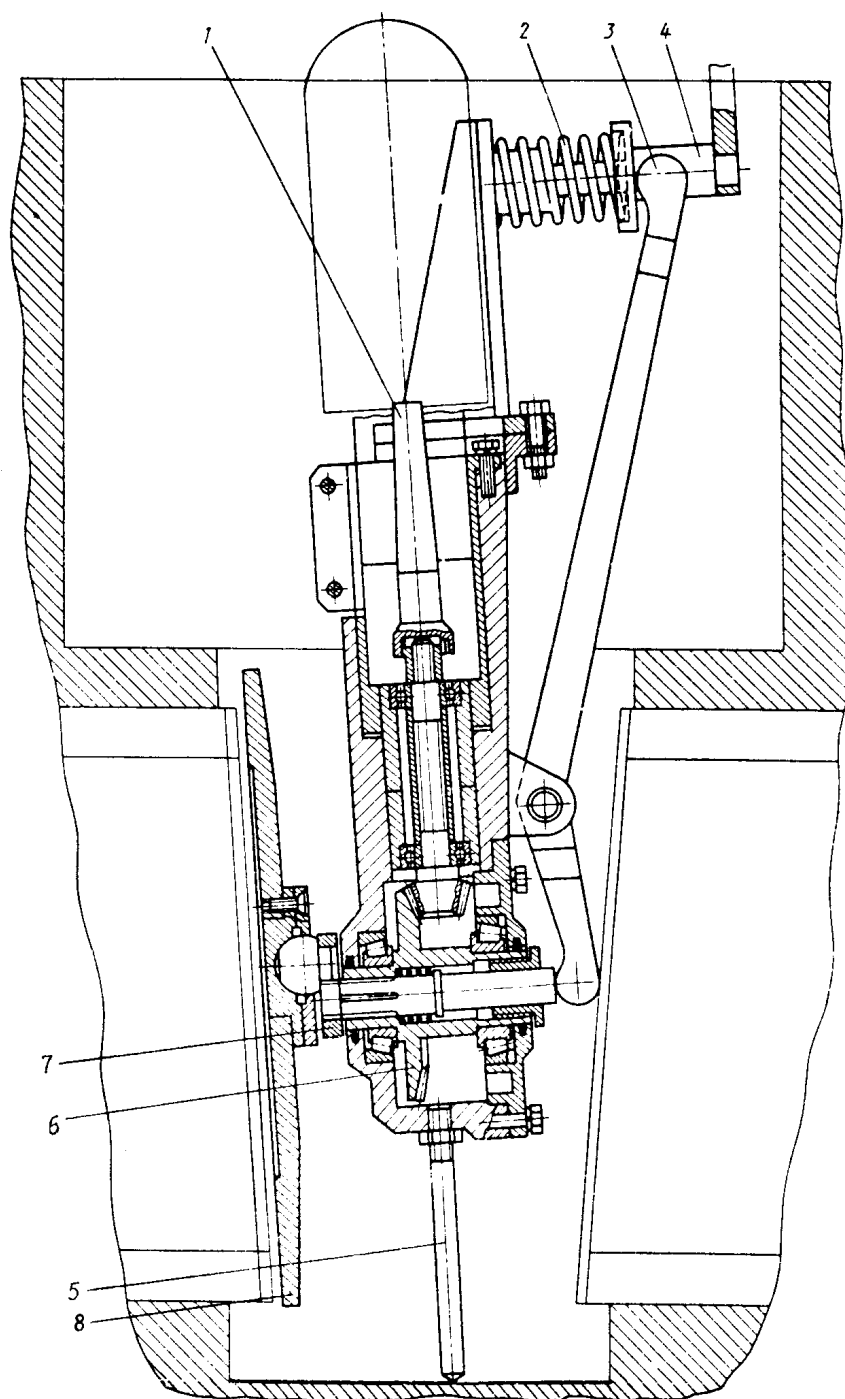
Приспособление для притирки уплотнительных поверхностей задвижек с D_y 250—300 мм.
